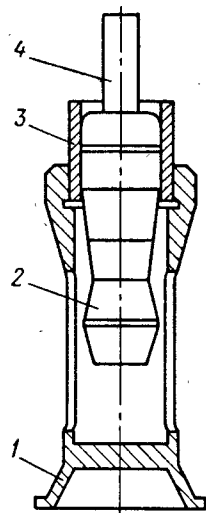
Схема приспособления для пропитки пористого бронзового слоя, напеченного на внутреннюю поверхность стальной втулки
